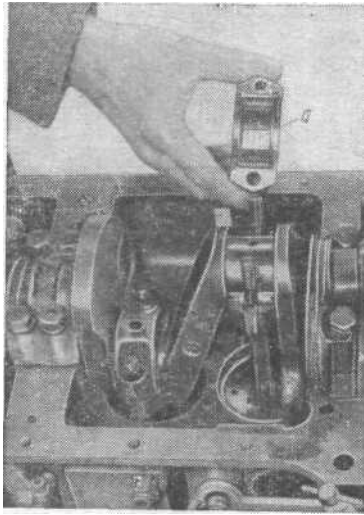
Укладка контрольной пластинки-щупа в шатунный подшипник:
